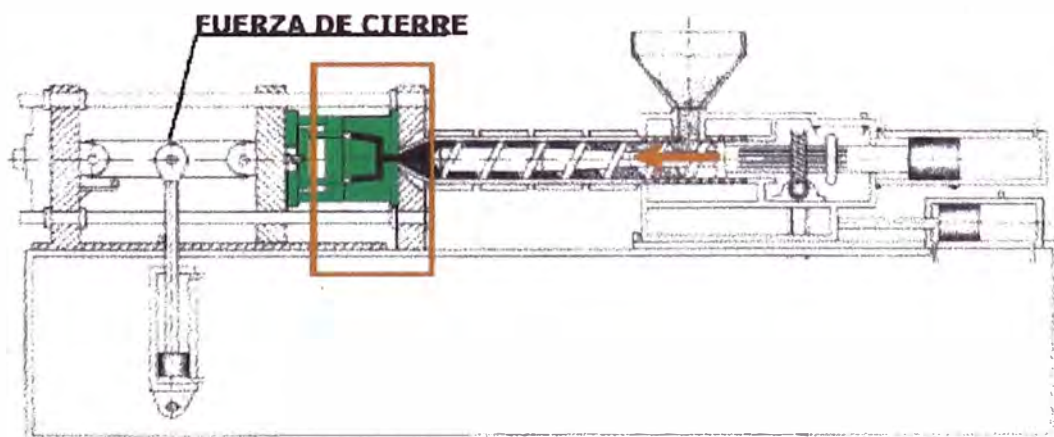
Máquina de Inyección de Husillo Reciprocante con molde cerrado
